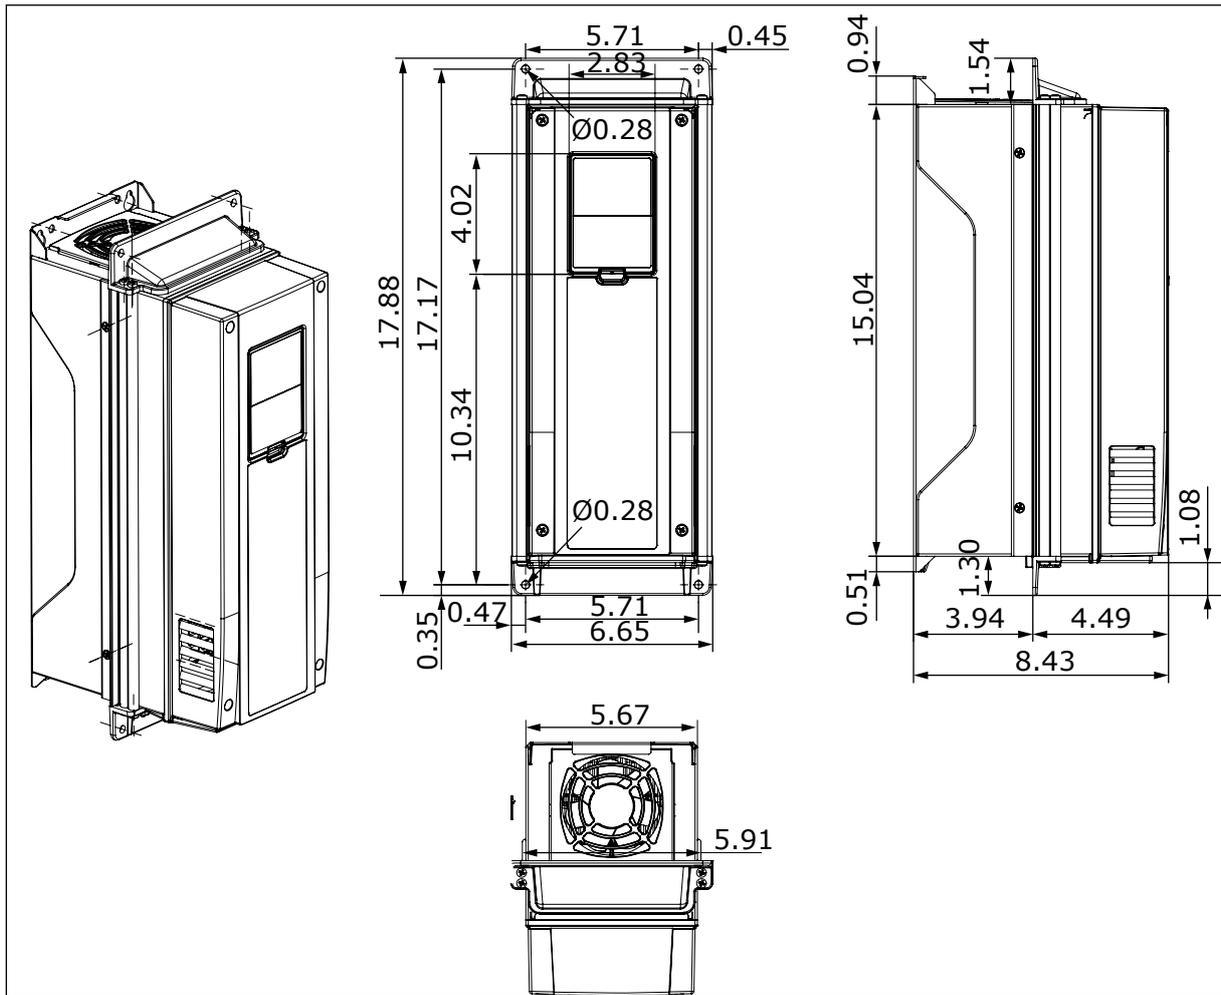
Abmessungen des Frequenzumrichters, Flanschbefestigung, MR5 [in]
